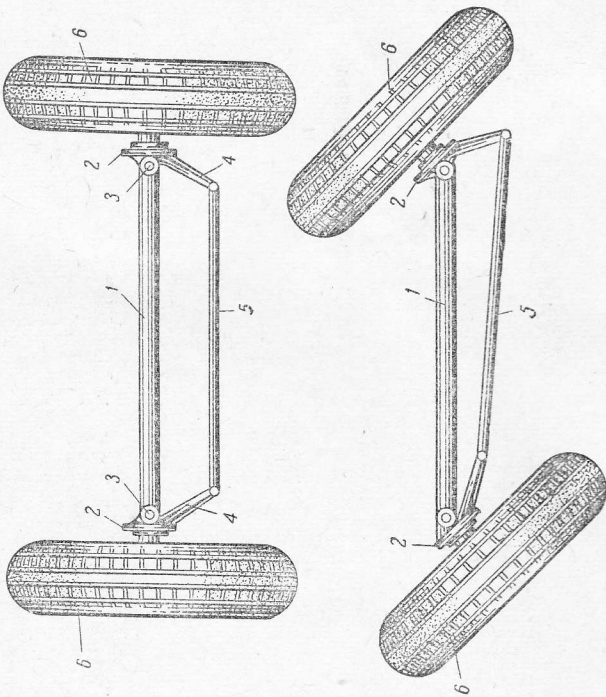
Схема устройства рулевой трапеции и расположения ее деталей при повороте колес:
